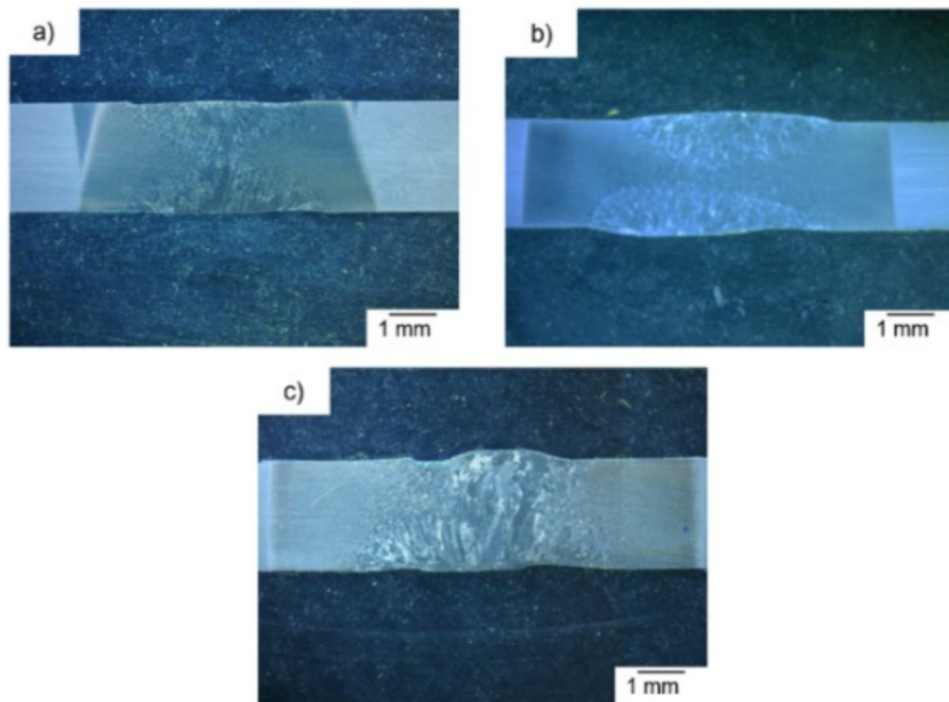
Macrográficas mediante estereoscopia a 6.5x para uniones de acero HSLA: a) GTAW5 sin defectos de soldadura, b) GTAW1 con desfaseamiento entre cordones y c) GTAW6 con cordón de respaldo de mayor tamaño que de relleno [10].
